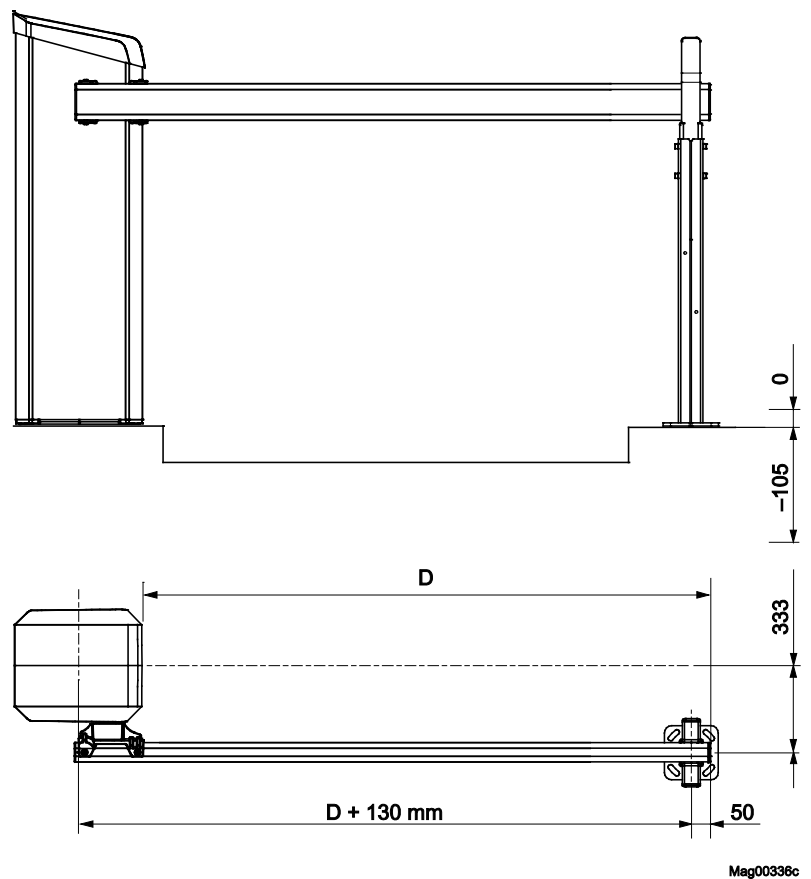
Abmessungen Schrankengehäuse – Pfosten (Maße in mm)
